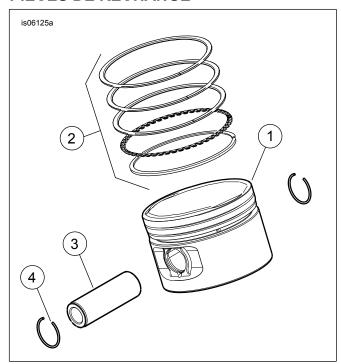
Pièces de rechange : Kits de pistons avant et arrière
